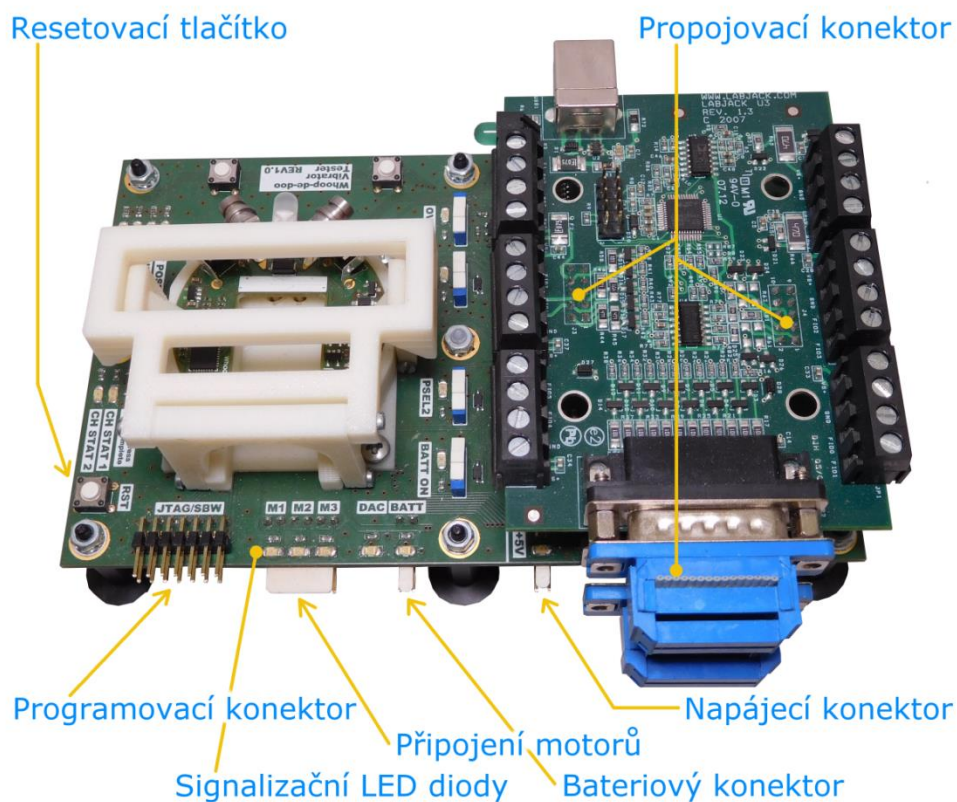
Příklad upínání výrobku do platformy při testování.
